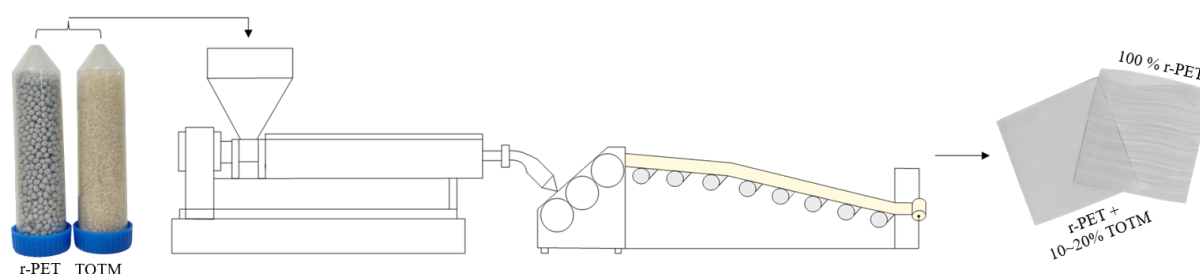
Esquema de extrusão seguida de moldagem de filmes com bobinamento por calandras
